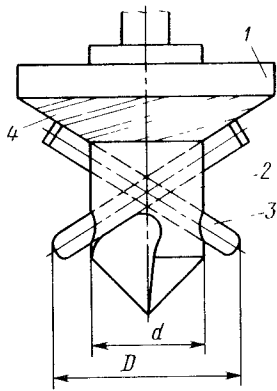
Инструмент для сверления технологического отверстия и отбортовки развальцовкой
